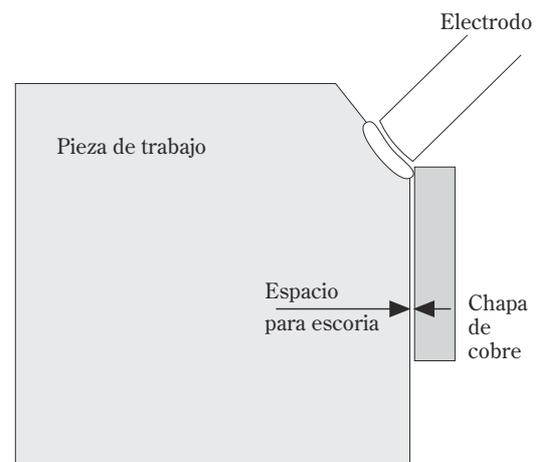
Chapa de cobre como soporte de la soldadura al reconstruir esquinas.
